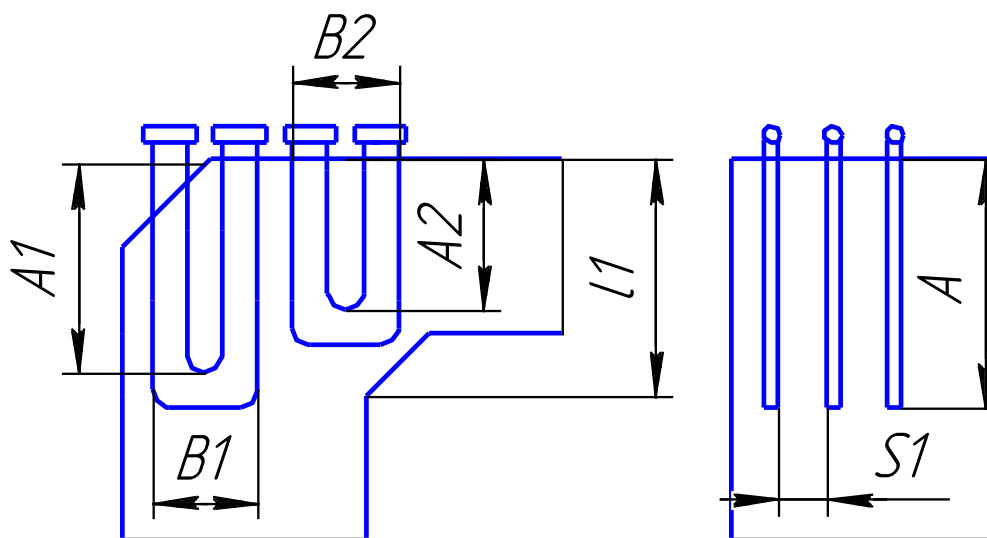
Конструктивные размеры ширмового пароперегревателя
